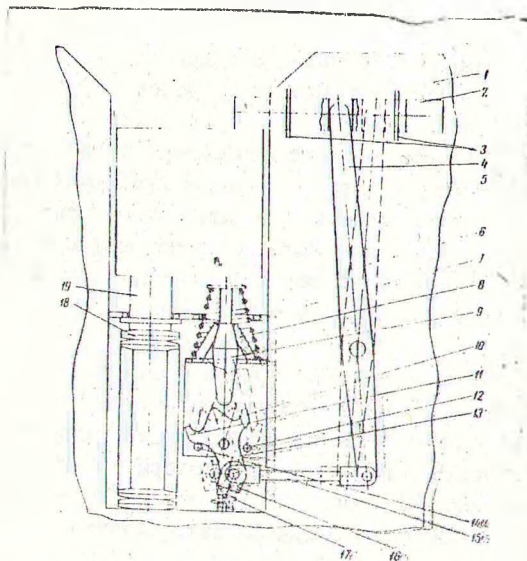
Замок крепления дышла: 1-ограждение кабины; 2-запорный стержень; 3-направляющая запорного стержня; 4-двухплечий рычаг; 5-дышло; 6, 17-пружины; 7-пластину; 8-гнездо толкателя; 9-толкатель; 10, 11, 16 - плечи трехплечего рычага; 12, 14-упоры; 13-трехплечий рычаг; 15-тяги; 18-пружина тарельчатая; 19-упор.
